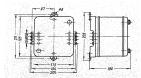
Габаритные и установочные размеры ре-ле типа ЭТ-523/1Д с передним присоединением
